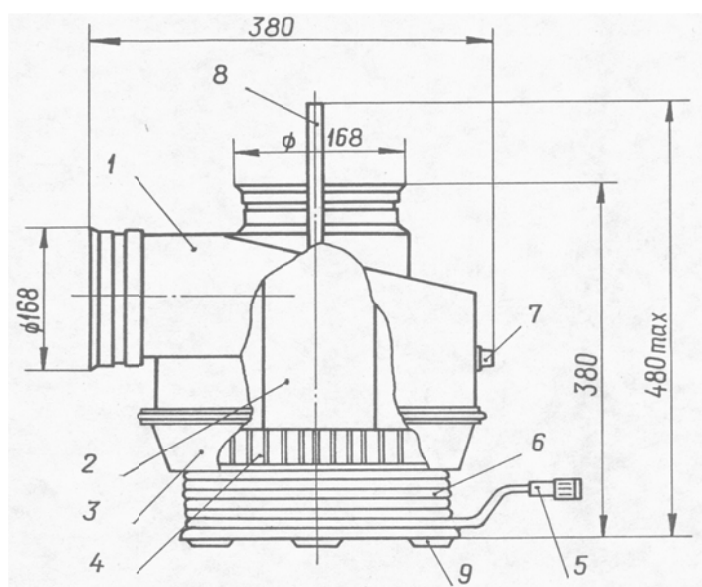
Центробежный вентилятор агрегата «Шмель-2500»:
